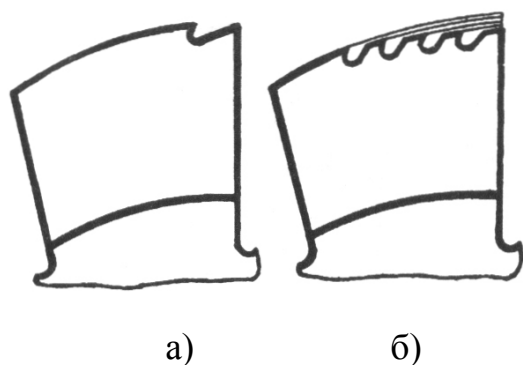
Зуб червячной фрезы с дополнительными вершинными одной (а) или несколькими (б) режущими кромками
